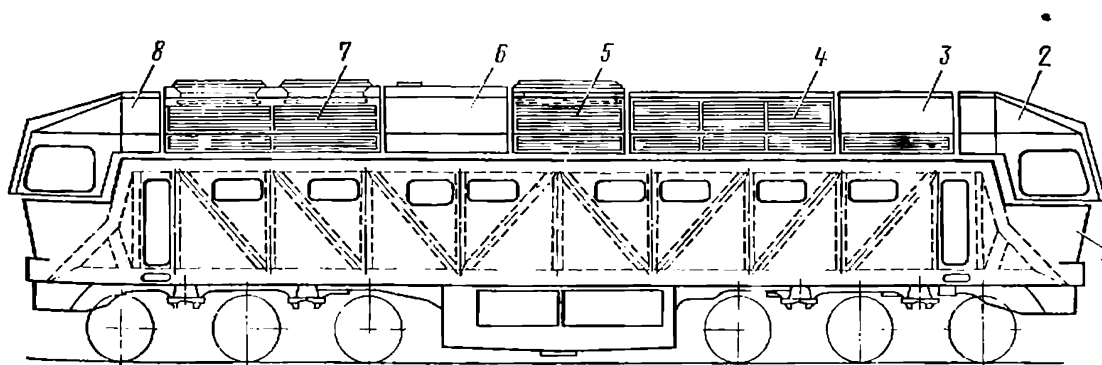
Конструктивная схема кузова со съемными крышами блочного типа: 1 — несущий остова с рамой; 2 — блоки крыш кабин машиниста; 3 — крыша над высоковольтной камерой; 4 — блок фильтров централизованного воздухообеспечения; 5, 7 — блоки охлаждающего устройства одинарный и двойной; 6 — блок глушителя
